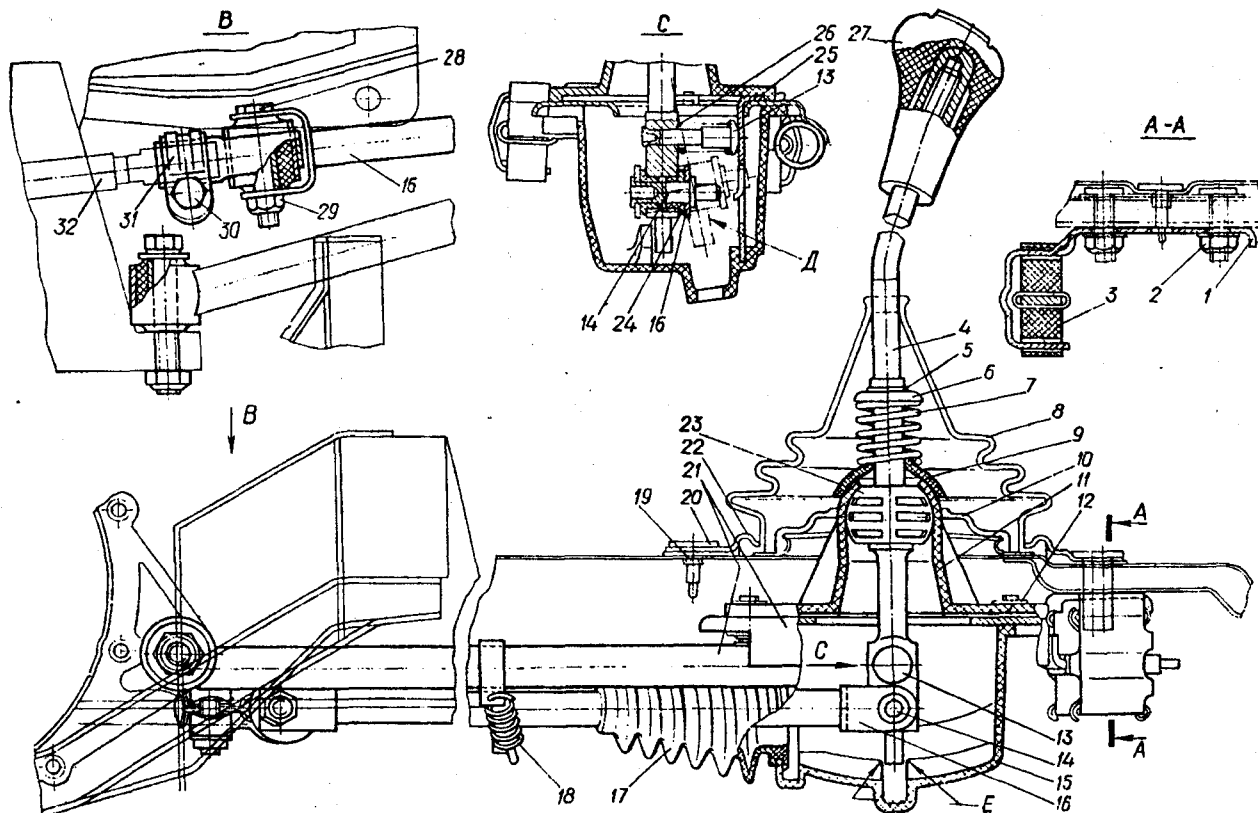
Механизм управления переключением передач: 1 – наружный кронштейн крепления механизма; 2 – гайка крепления механизма; 3 – муфта резиновая крепления основания; 4 – рычаг переключения передач; 5 – стопорное кольцо; 6 – шайба стопорная; 7 – пружина рычага; 8 – чехол рычага; 9 – чашка упорная; 10 – уплотнитель привода; 11 – опора шаровая; 12 – втулка опоры; 13 – упор подвижный; 14 – упор неподвижный (направляющий); 15 – крышка привода; 16 – вал управления; 17 – чехол защитный; 18 – пружина возвратная; 19 – втулка поршня; 20 – поршень; 21 – основание привода с реактивной штангой; 22 – крышка чехла верхняя; 23 – сферическая головка (шарик рычага); 24 – втулка опорная; 25 – кронштейн упора; 26 – пружина подвижного упора; 27 – рукоятка рычага; 28 – болт стяжной; 29 – гайка крепления реактивной штанги; 30 – болт крепления хомута; 31 – хомут; 32 – (хвостовик) ползун коробки передач; Д – положение рычага при установке и регулировке привода управления механизмом переключения передач, соответствующее выбору пятой передачи – заднего хода; Е – нейтральное положение рычага
